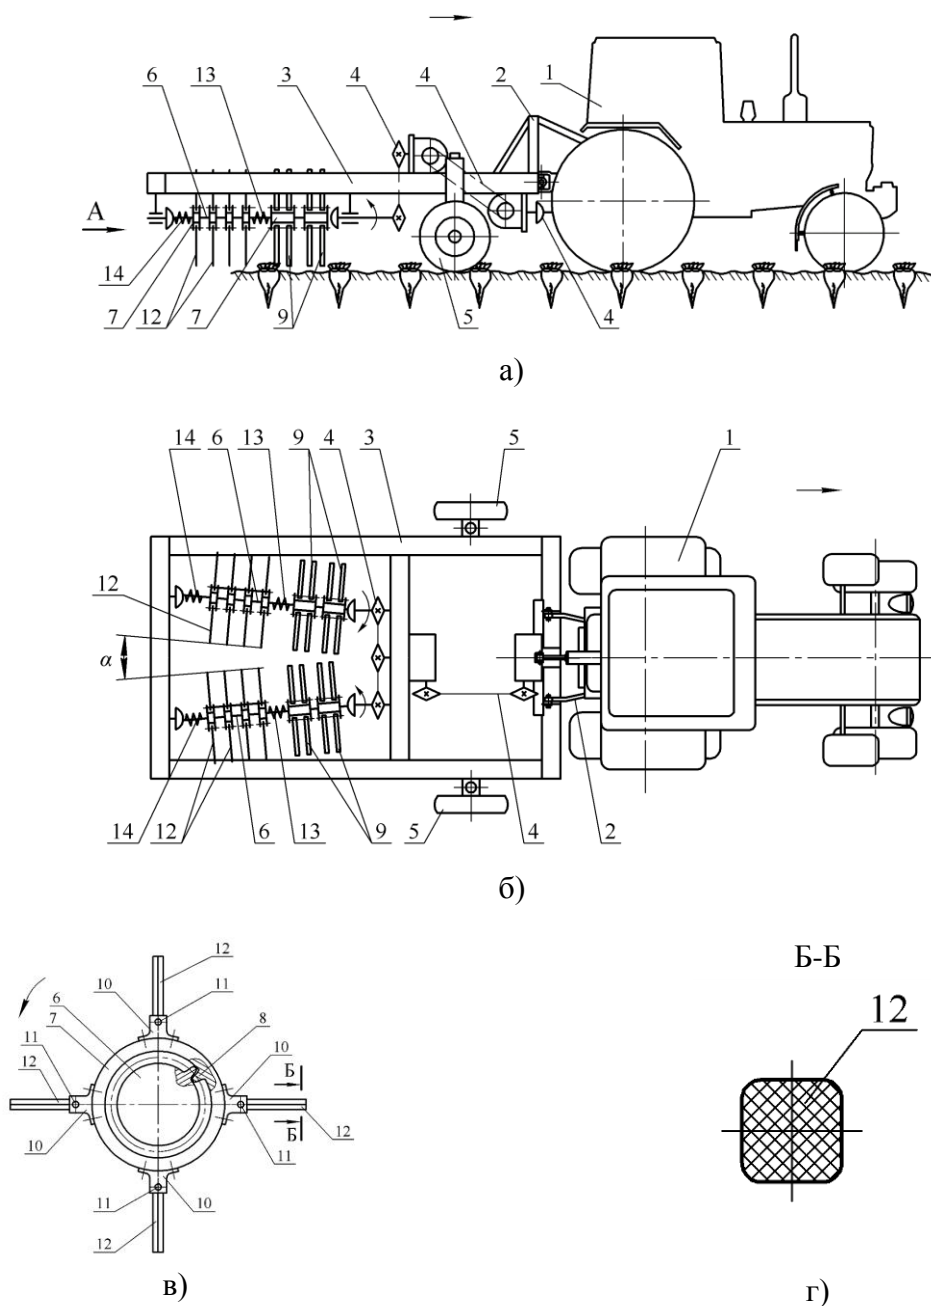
Конструктивна схема агрегату для очищення головок коренеплідних культур від залишків гички на корені: а) вигляд збоку; б) вигляд зверху; в) вид А; г) переріз Б-Б
